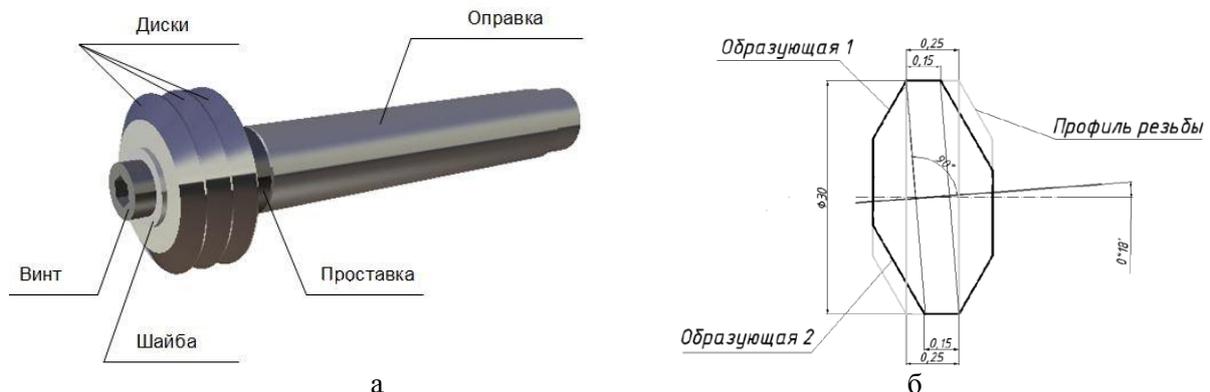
Конструкция инструмента: а - инструмент в сборе, б - деформирующее кольцо.
